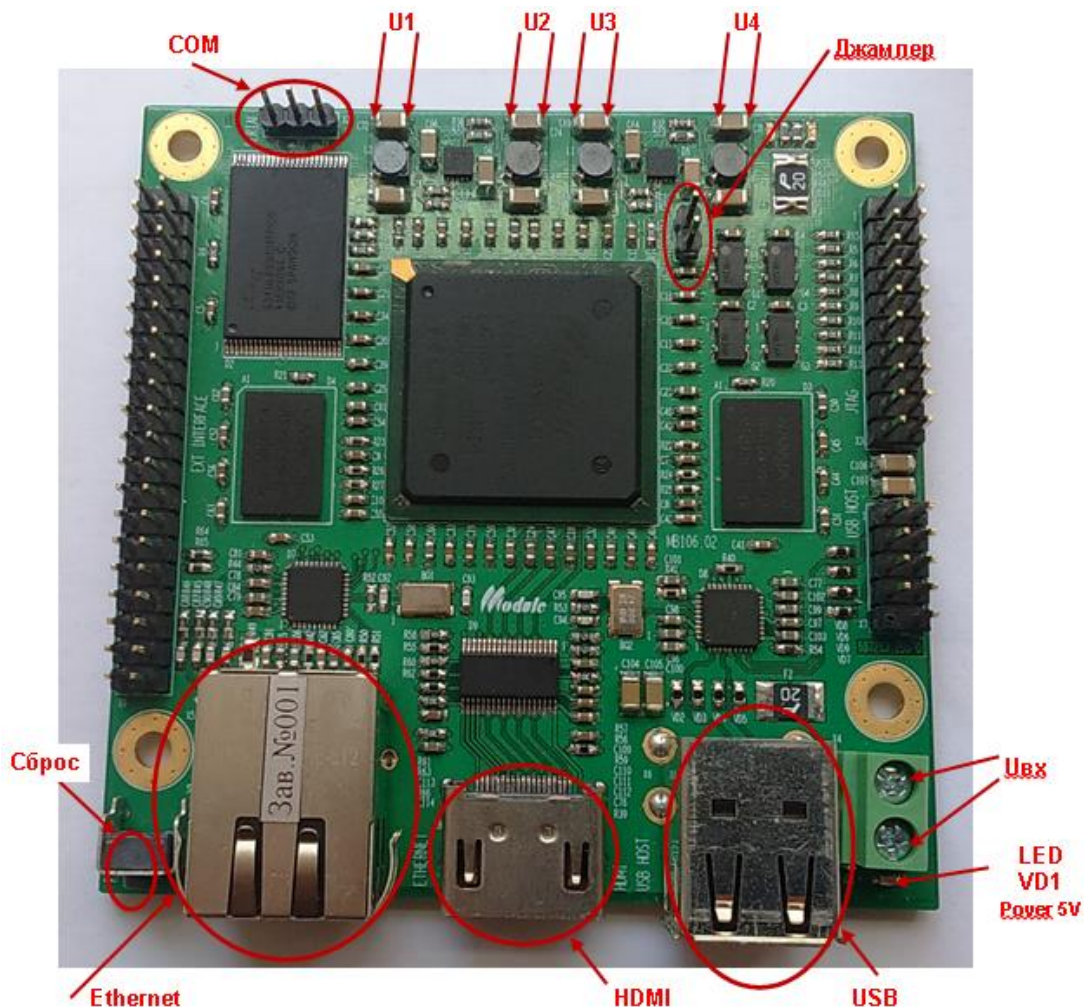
Внешний вид модуля и точки измерения напряжений
